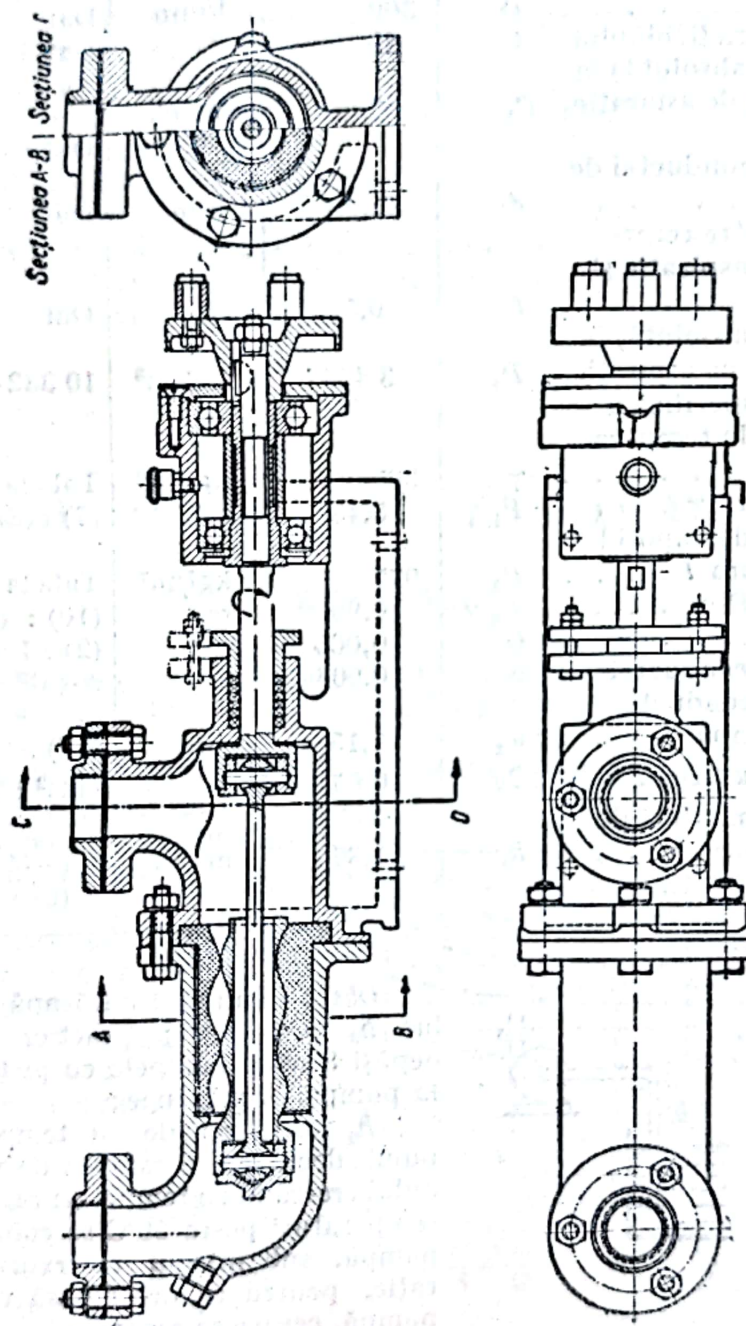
Pompă cu piston rotativ — sistem șurub.
